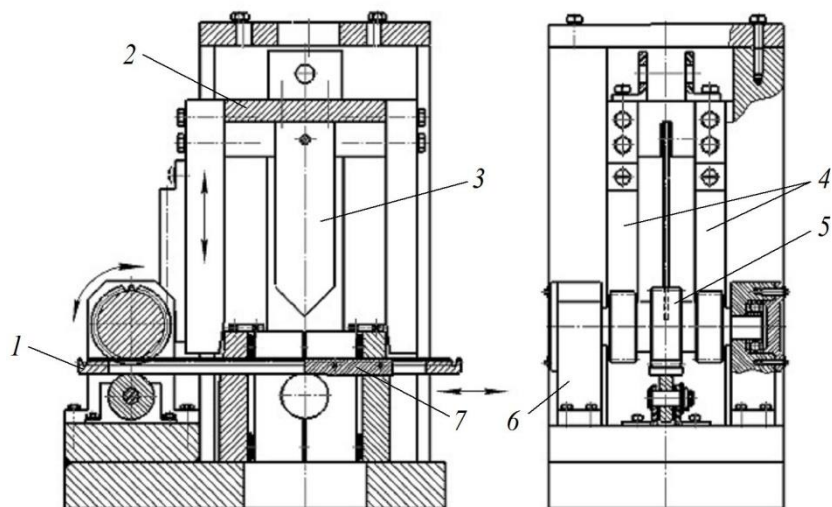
Кинематическая схема механической синхронизации движения горизонтального и вертикального ножей режущего блока ножниц: 1 – горизонтальная зубчатая рейка; 2 – суппорт; 3 – вертикальный клиновидный нож; 4 – вертикальные зубчатые рейки; 5 – вал с зубчатыми колесами; 6- подшипниковая опора вала; 7 – горизонтальный нож
